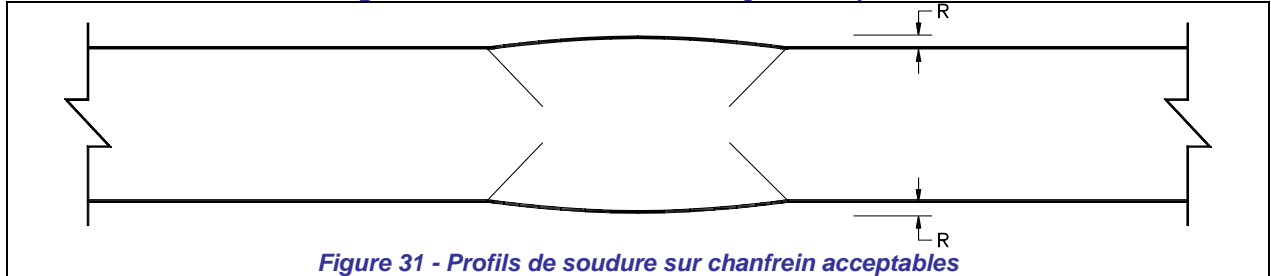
Profils de soudure sur chanfrein acceptables
